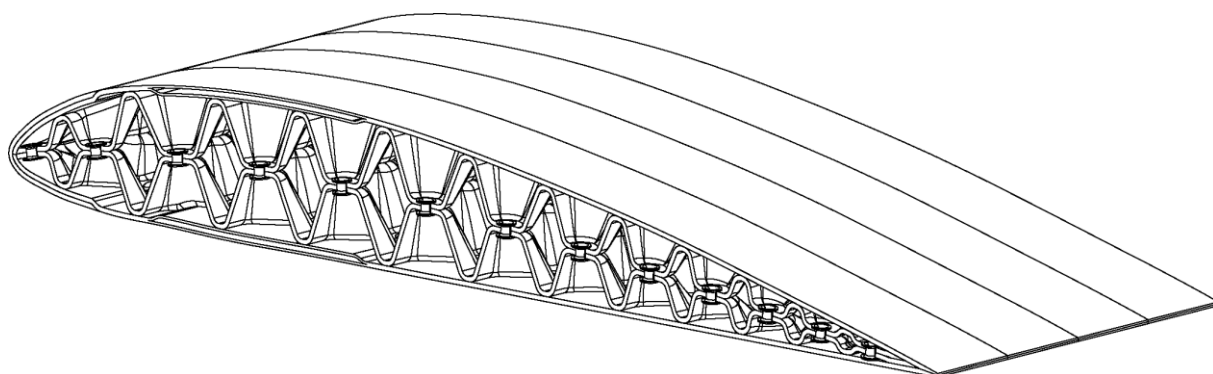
Общий вид получаемой конструкции многослойной несущей поверхности с дискретным наполнителем
